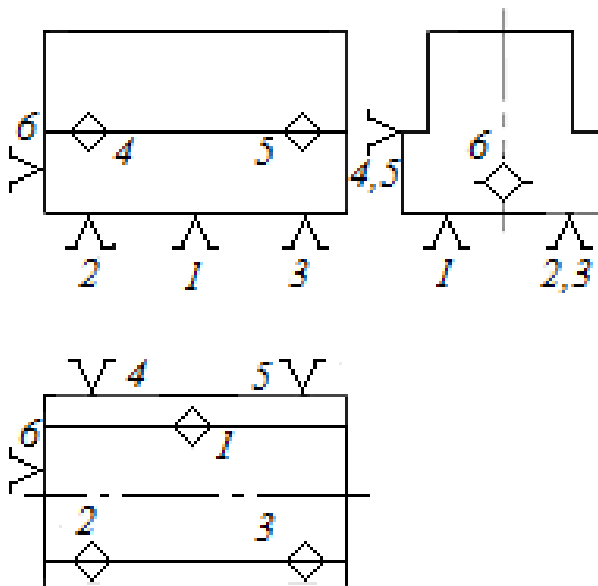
Чистові ТБ при базуванні по трьох зовнішніх оброблених поверхнях
